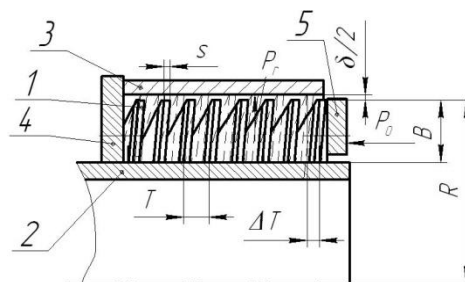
Розрахункова схема геометричних параметрів затиску заготовки гвинтовим затискним елементом з конічними частинами: 1 – гвинтовий затискний елемент, 2 – корпус оправки, 3 – заготовка, 4 – упорне кільце, 5 – затискна втулка
